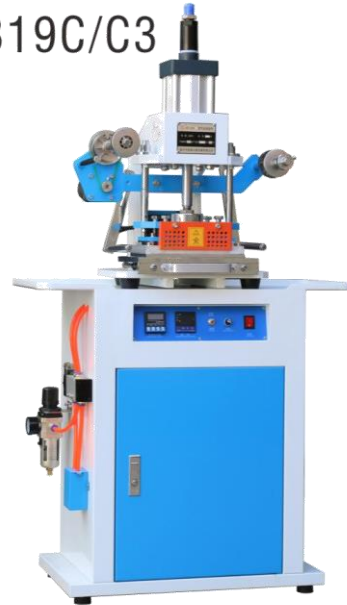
Máquina de estampación neumática para elementos de cuero. Adaptado de (NEJE Industrial Machines, 2019).
